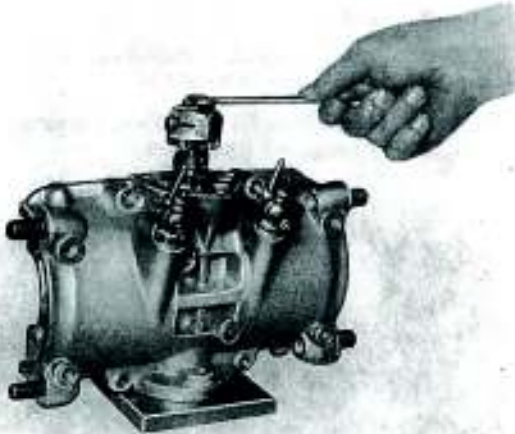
Gegenhalter in Ringrillenlagerbohrung stecken und Mutter lösen
